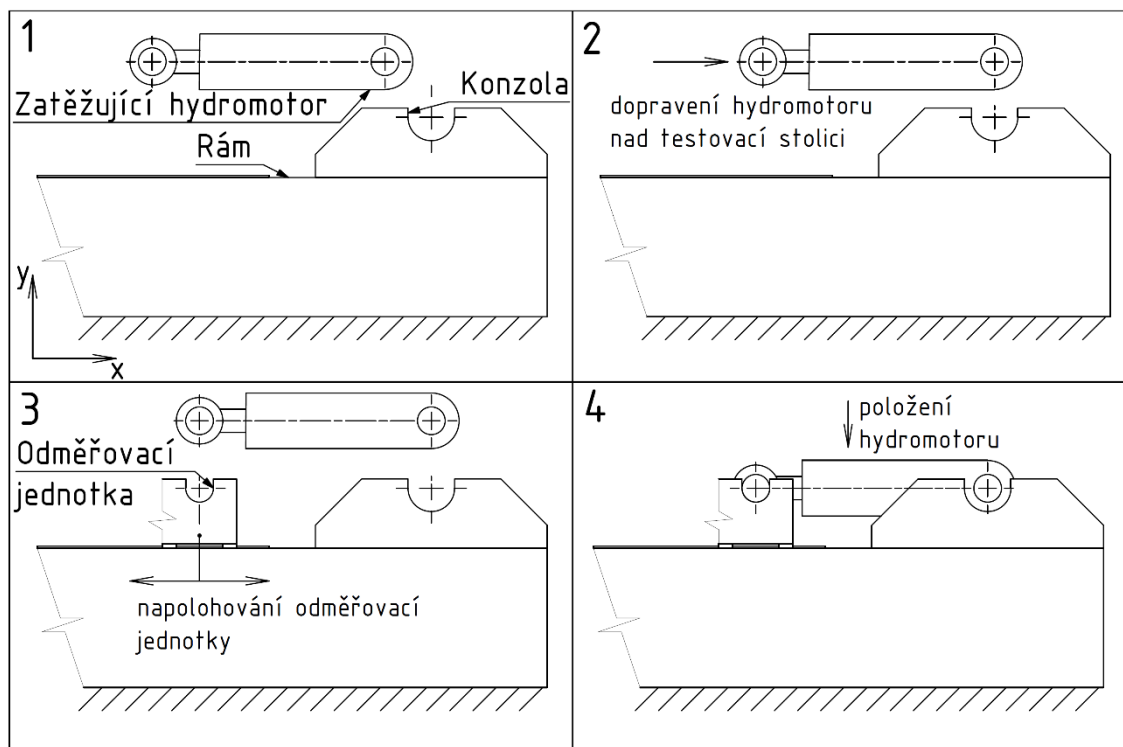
Testovací stolice Hengli 2P2F [2]
